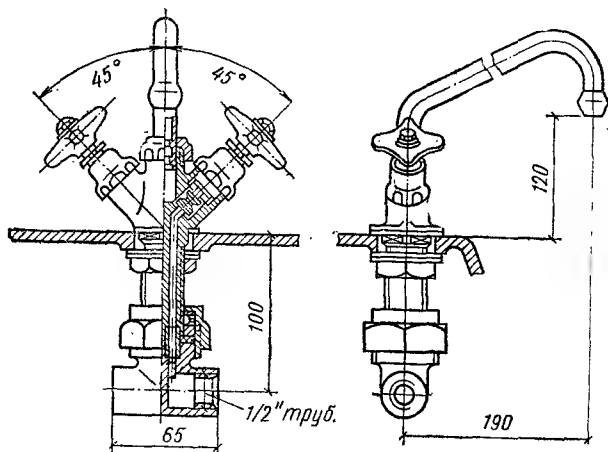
Смеситель для мойки центральный См-М-ВКСЦ
